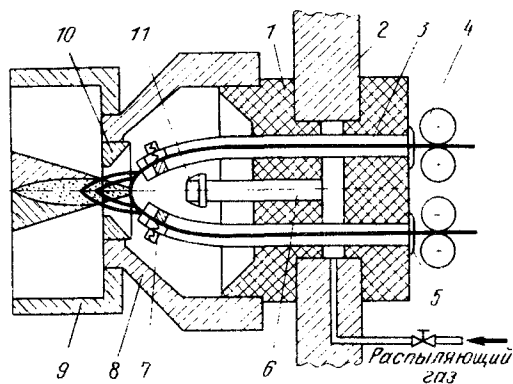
Конструктивная схема распылительной головки электродугового металлизатора
